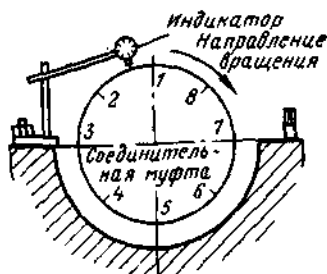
Проверка эллипсности (биения) полумуфты ротора
